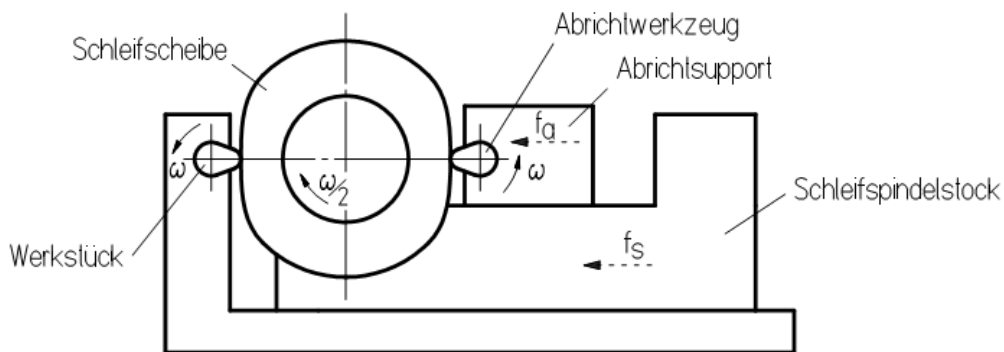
Unrunder Abrichten der Schleifscheibe mit einem unrunder Abrichtwerkzeug
